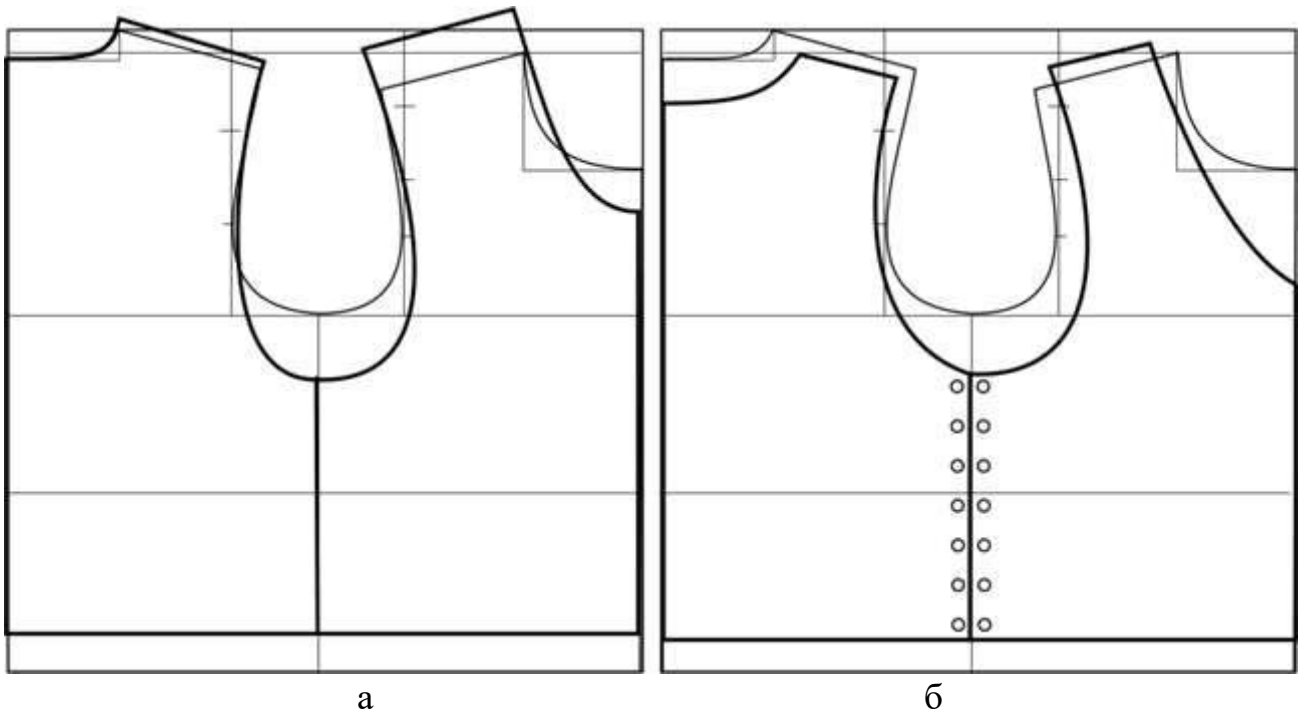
Схема деталей конструкції базового розвантажувального жилету М1 (а) та М2 (б)
